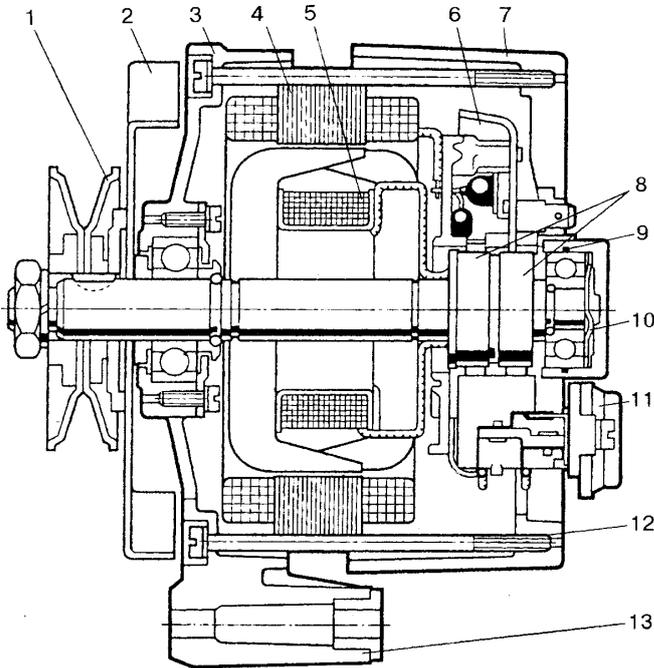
Внутреннее устройство генераторов К.1, NI фирмы Bosch: I - шкив; 2 - вентилятор; 3, 7 - передняя и задняя крышка; 4 - статор; 5 - обмотка возбуждения; 6 - выпрямительный блок; 8 - контактные кольца; 9 - резиновое кольцо; 10 - прижимная шайба; II - узел "щеткодержатель-регулятор напряжения"; 12-стяжной винт;
